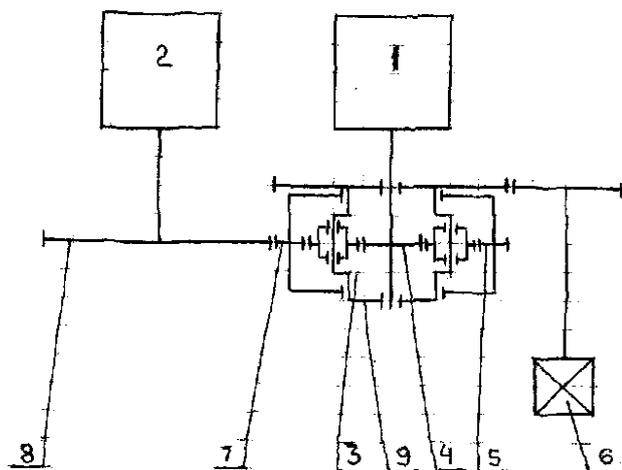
Кинематическая схема адаптивной системы трансмиссии привода двухбарабанного конвейера
